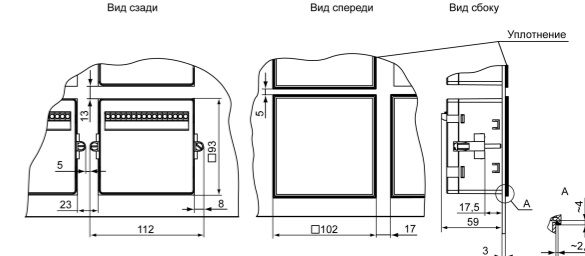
Прибор в корпусе Щ1, установленный в щит толщиной 3 мм
